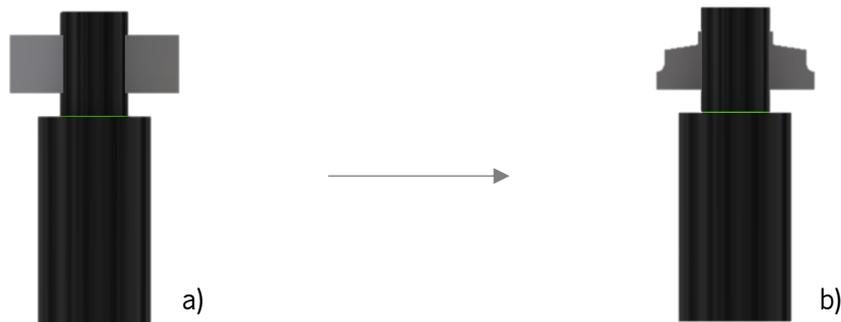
Ferramenta da família AÇO após o processo de a) Soldadura b) Fresagem HM
